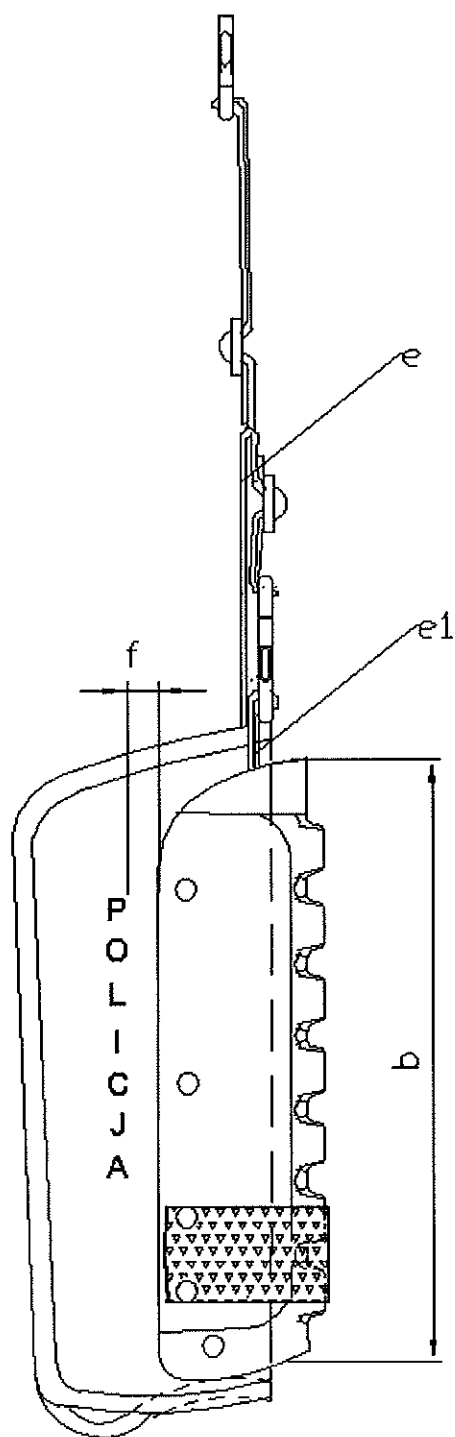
B – Ochraniacz przedramienia – widok od strony wierzchniej
